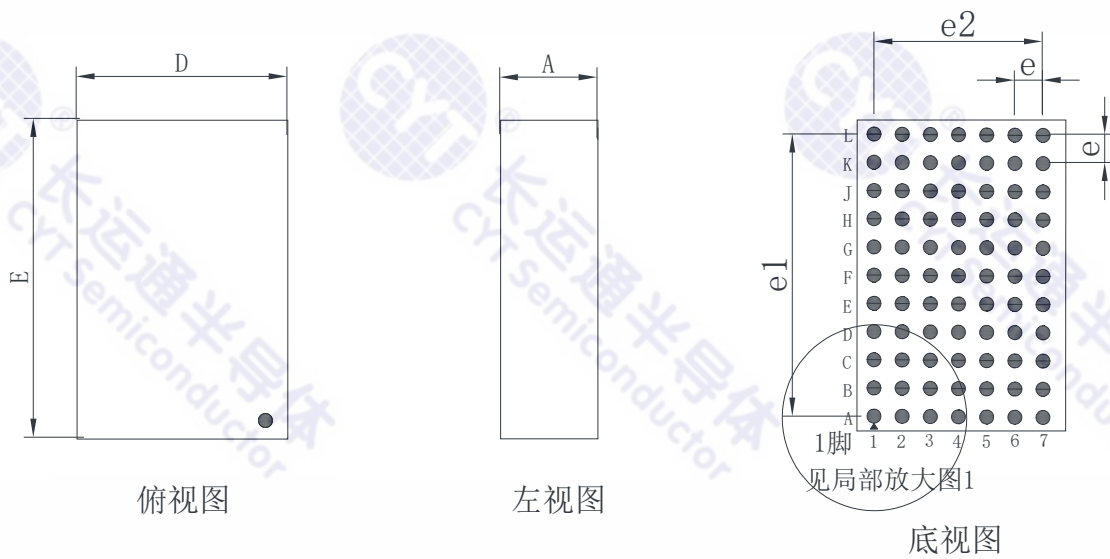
外形尺寸图 (9mm×15mm×5.01mm BGA77)
